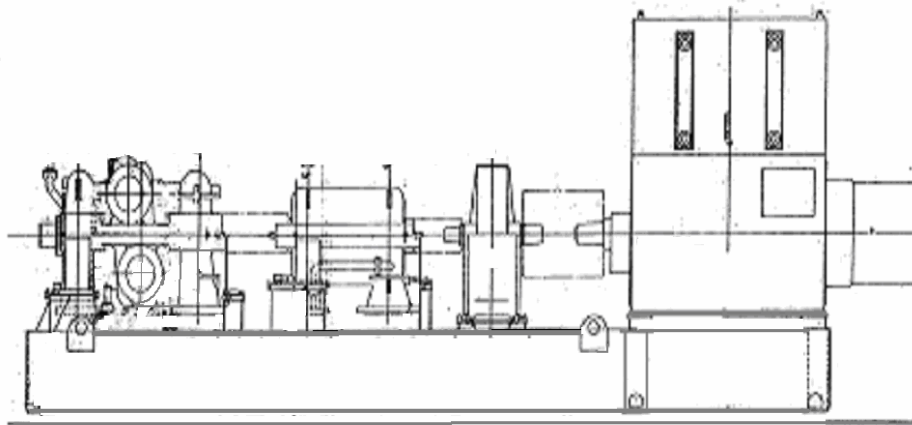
CONJUNTO COMPRESSOR 105-J
